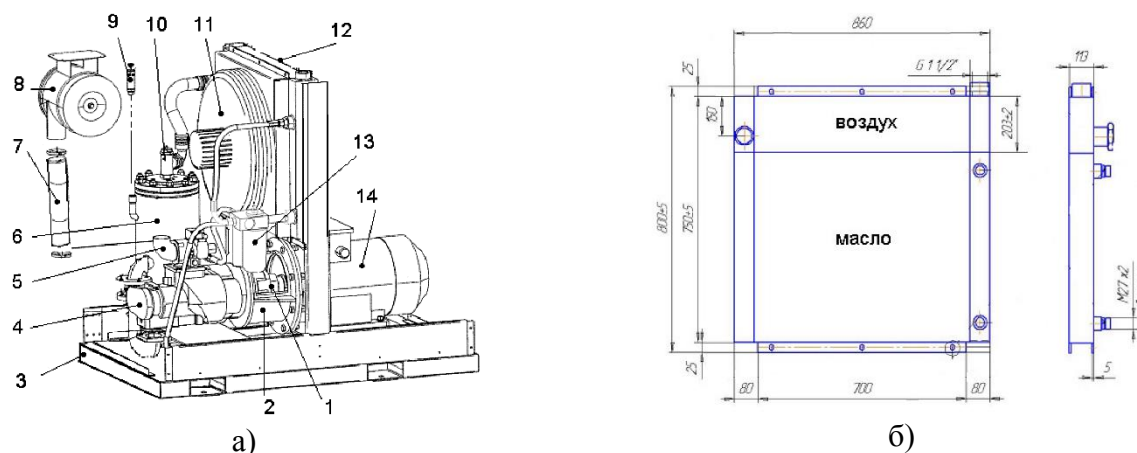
Компрессорная установка ДЭН-45ШМ
